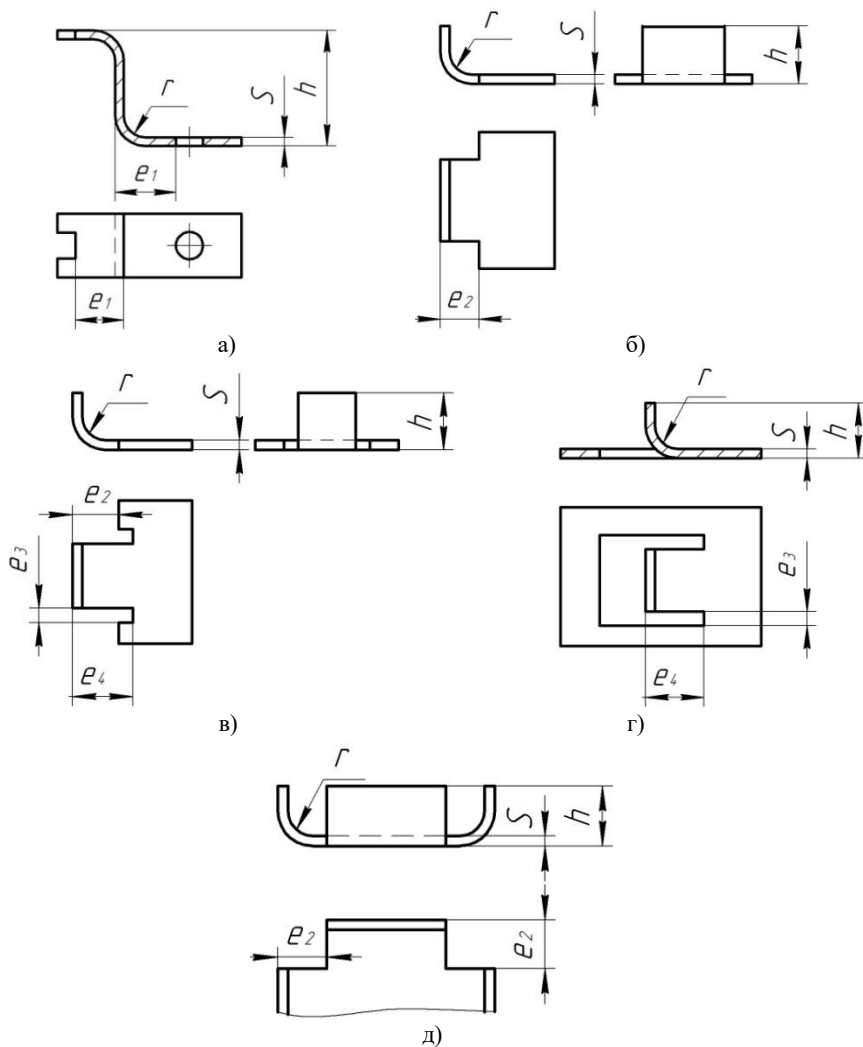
Варианты гибки: а) Z-образная деталь; б), в) V-образная деталь; г) надрезка с гибкой; д) деталь коробчатой формы
